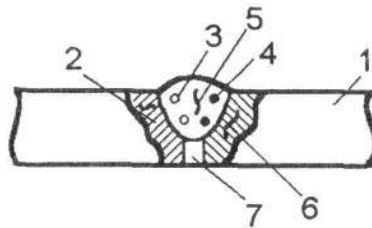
Внутрішні дефекти зварного шва: 1 – зварюваний метал; 2 – околошовна зона; 3 – газові пори; 4 – неметалеві включення; 5 – гарячі тріщини; 6 – холодні тріщини; 7 – непровар
